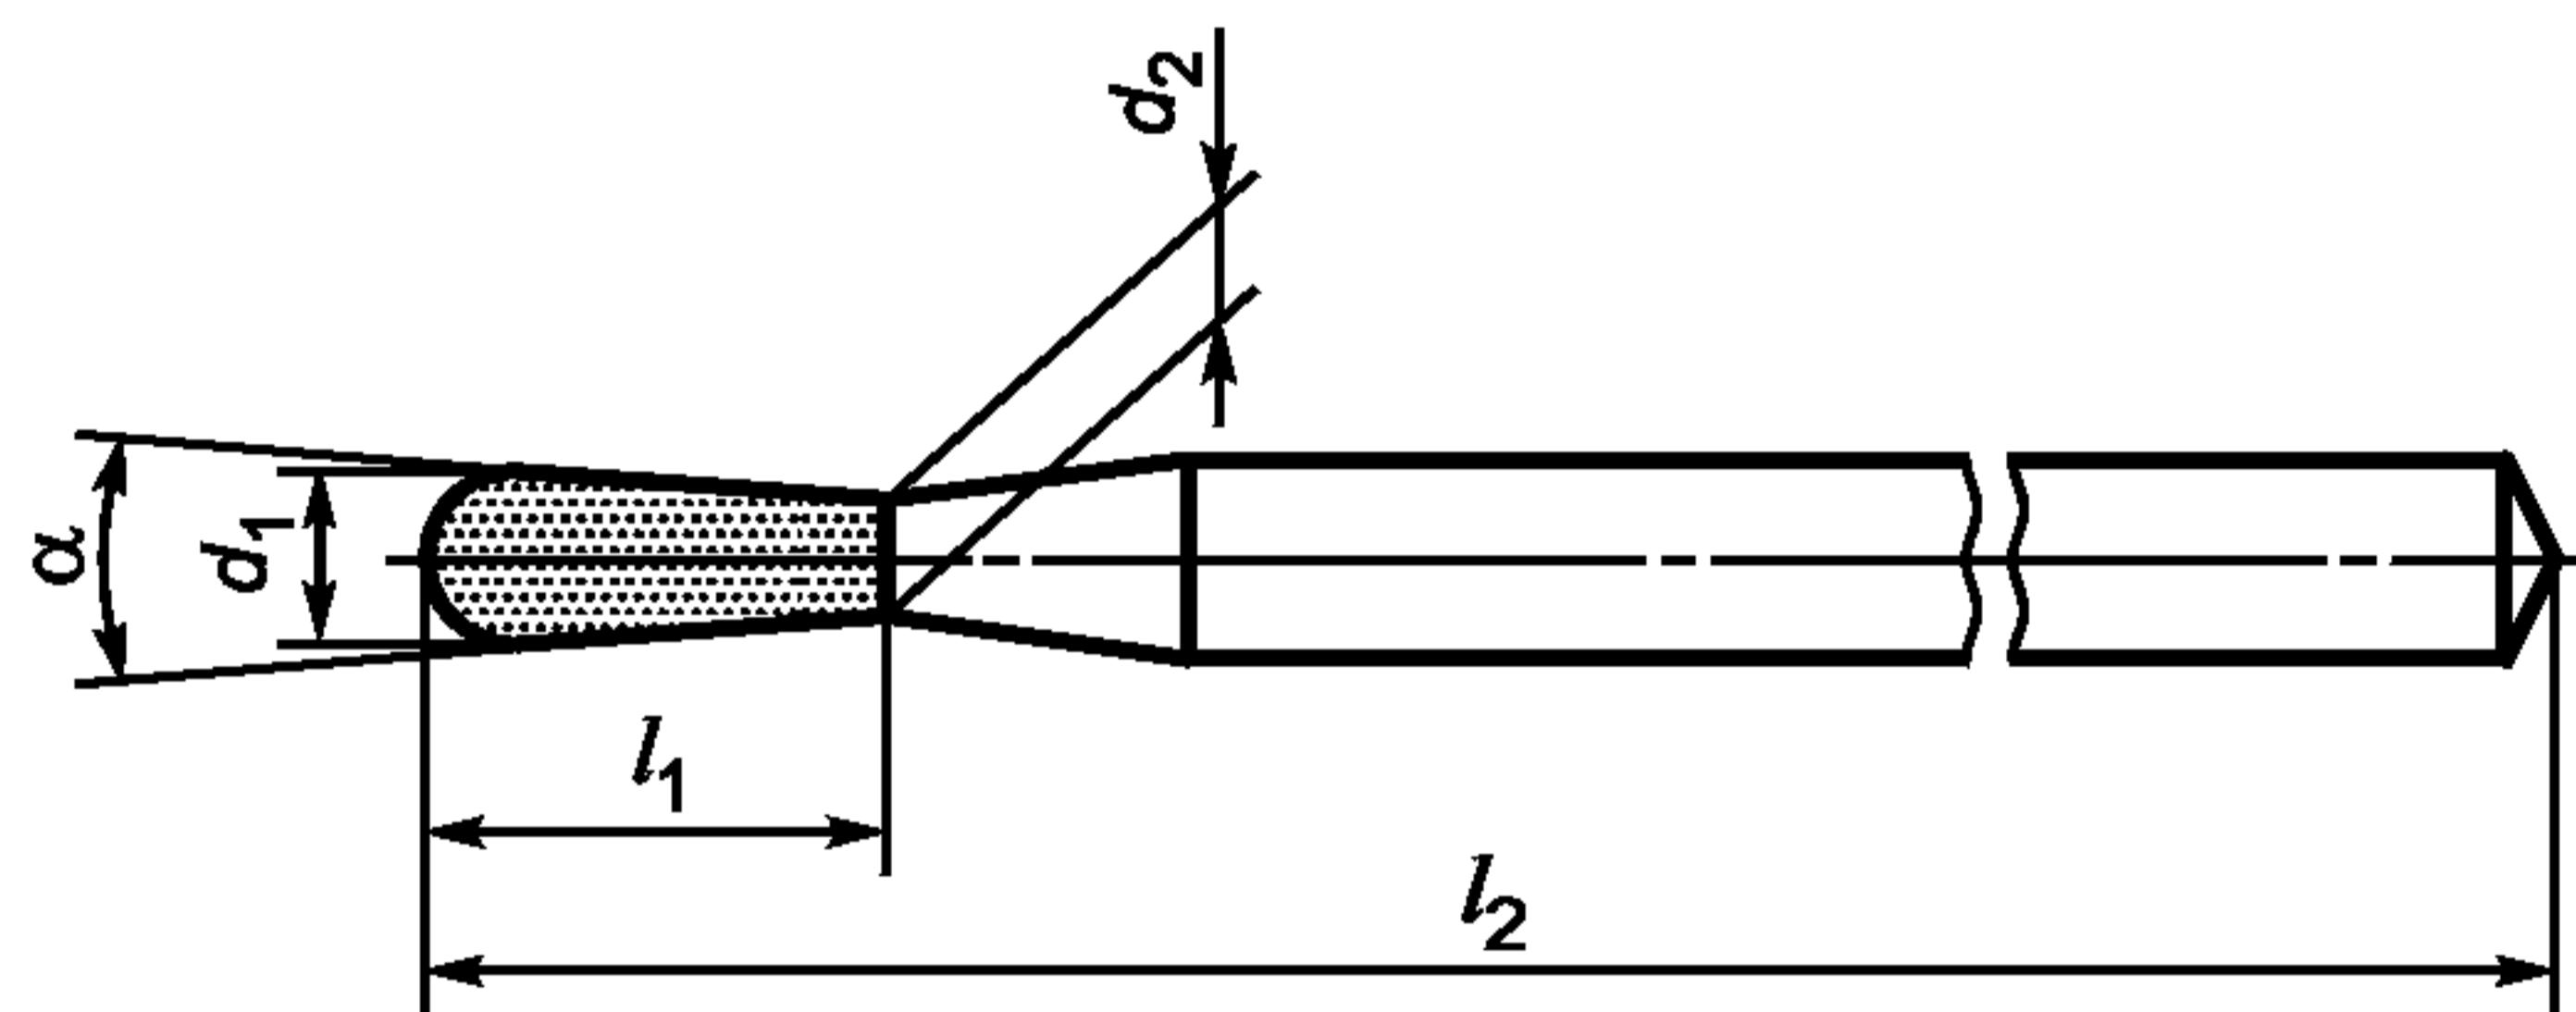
Полусферическая рабочая часть в форме обратно усеченного конуса с длиной головки 4,0 мм
